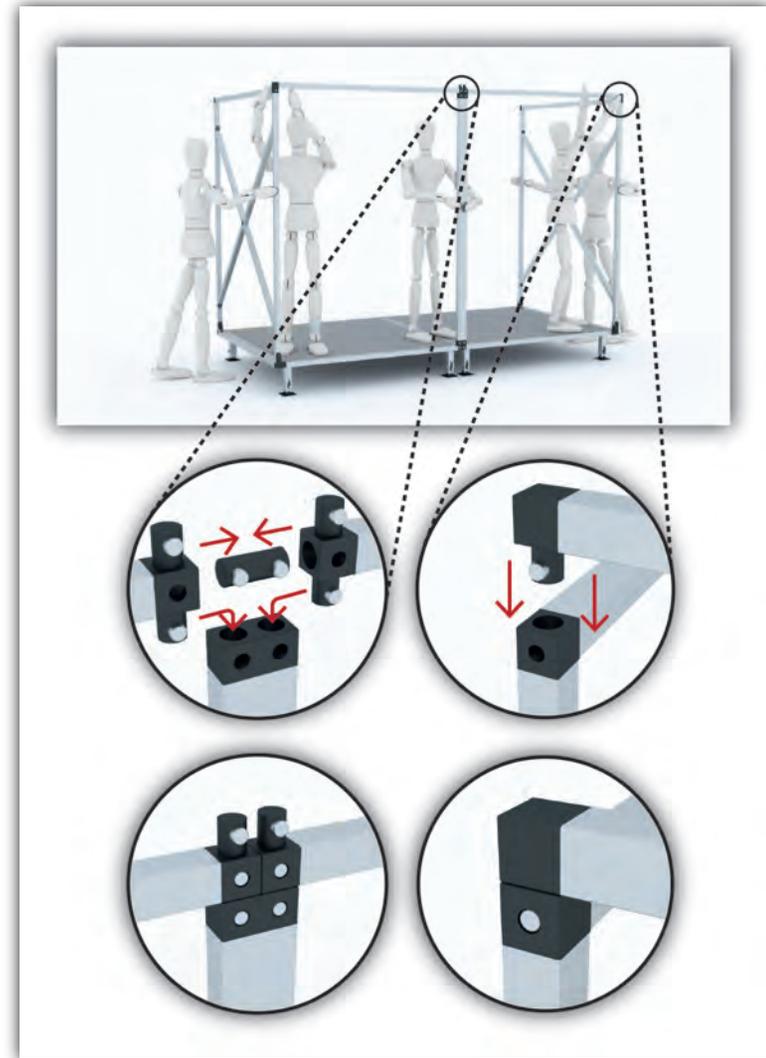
Ensamblaje de largueros de columna central con muros por medio de barril conector y ensamble con la parte superior de la columna central y con esquinas superiores de los muros.
